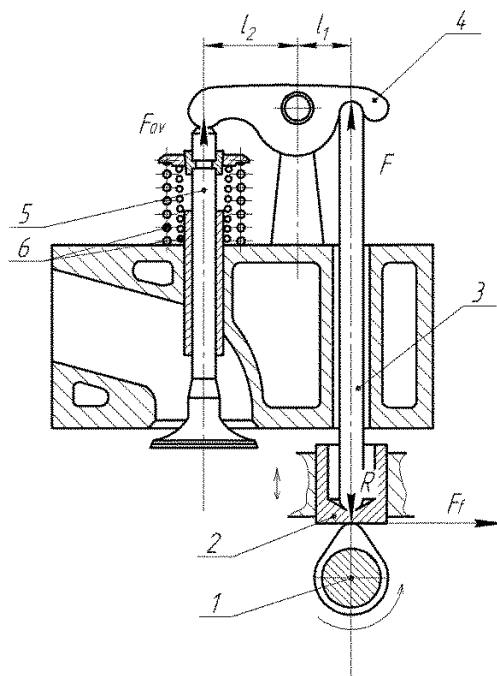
Схема сил, що діють в газорозподільному механізмі в момент відкриття клапана: 1 – розподільний вал; 2 – штовхач; 3 – штанга; 4 – коромисло; 5 – клапан; 6 – пружини
